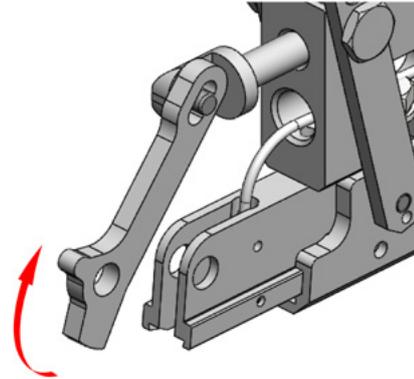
Werkzeug mit ausgebauten Frontabdeckungen
